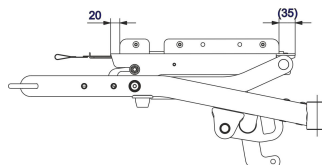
Sitsramens monteringsposition på sitsstöd utan körspärrfunktion
